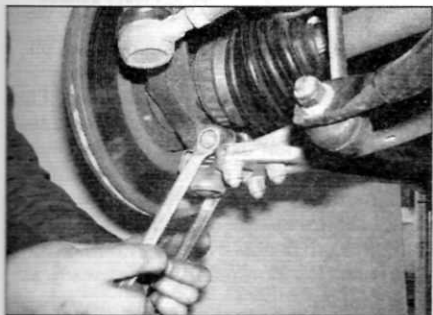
Отверните гайку и извлеките зажимной болт шарового шарнира нижнего рычага подвески из поворотного кулака
